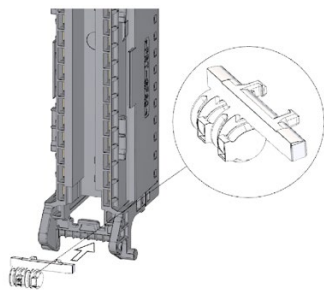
Mechanisches Kodierelement in neuen Frontstecker einsetzen
